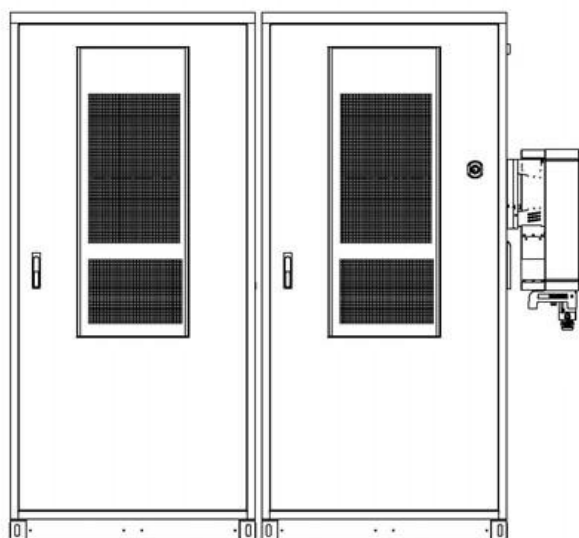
Collocazione degli armadi della batteria principale/secondario
